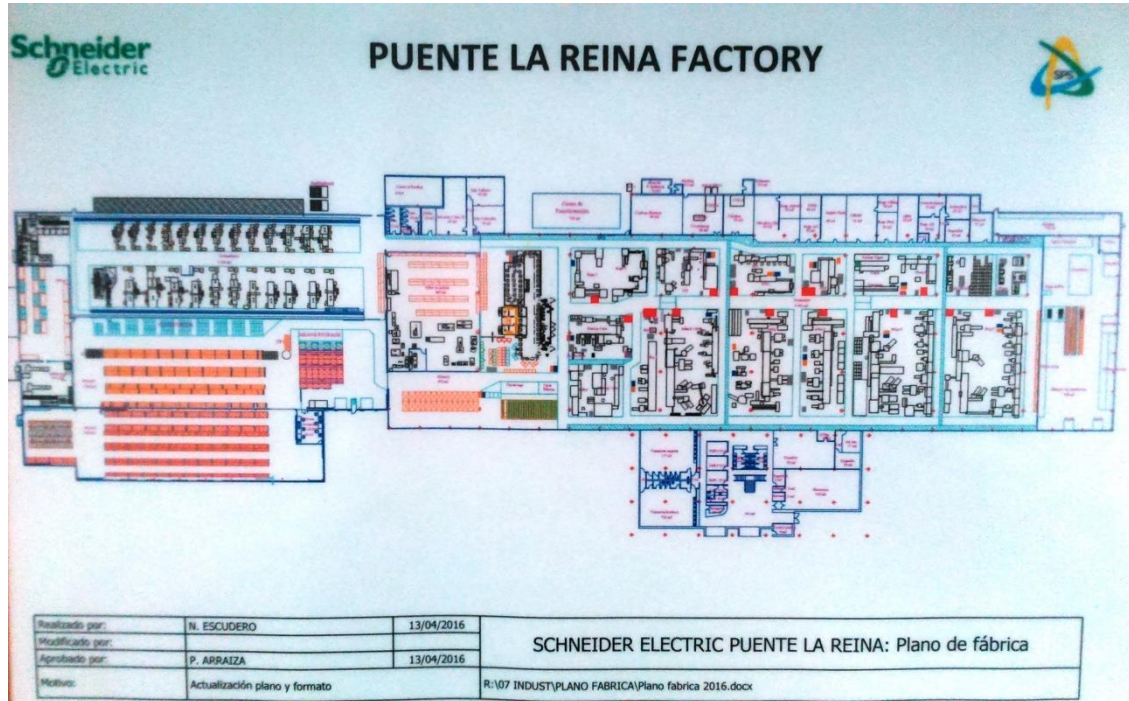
Plano en planta de la empresa Schneider Electric de Puente la Reina
